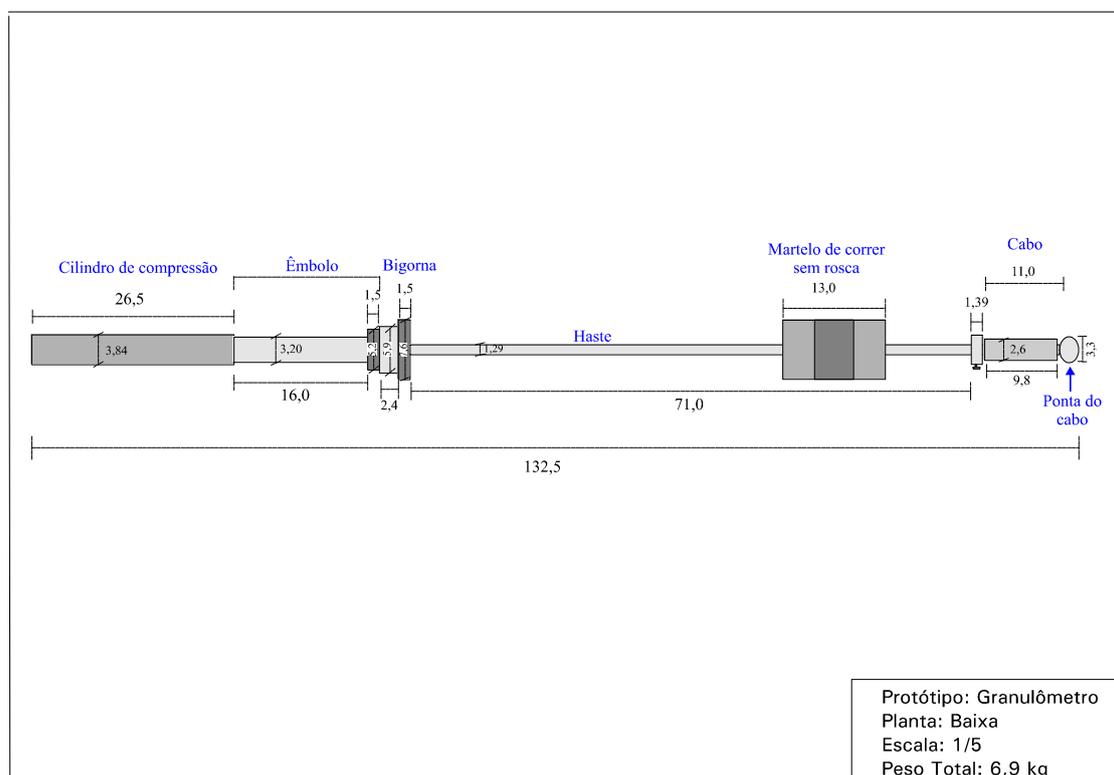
Planta baixa do granulômetro (medidas em cm).
